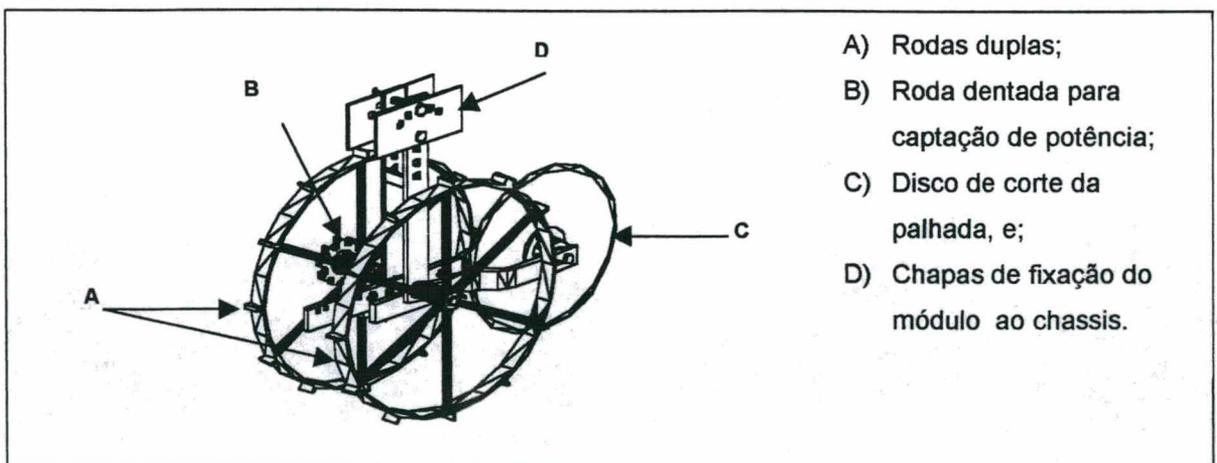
Desenho esquemático do Módulo Construtivo 03.
